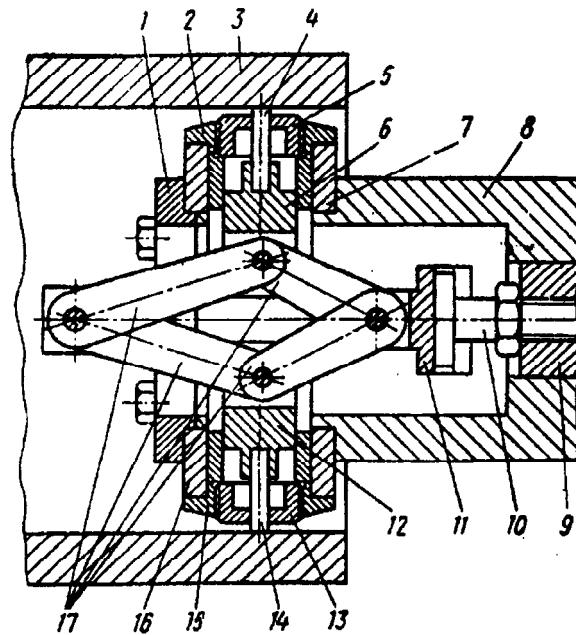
Схема пристосування для фрикційного латунювання гільзи циліндрів: 1 – кришка; 2 і 15 – направляюча втулка; 3 – оброблювальна поверхня; 4 і 14 – пруток; 5 і 13 – гайка; 6 і 12 – рухливий шток; 7 і 16 – стакан; 8 – голівка; 9 – підпружинена тяга; 10 – болт; 11 – вилка; 17 – важелі.
